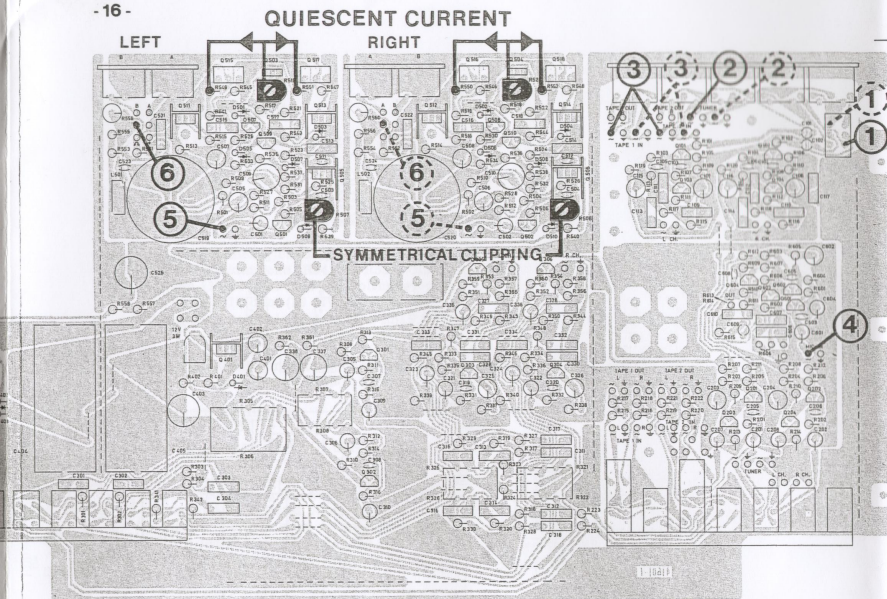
Hovedkort fra APPARAT NR. 1220501
